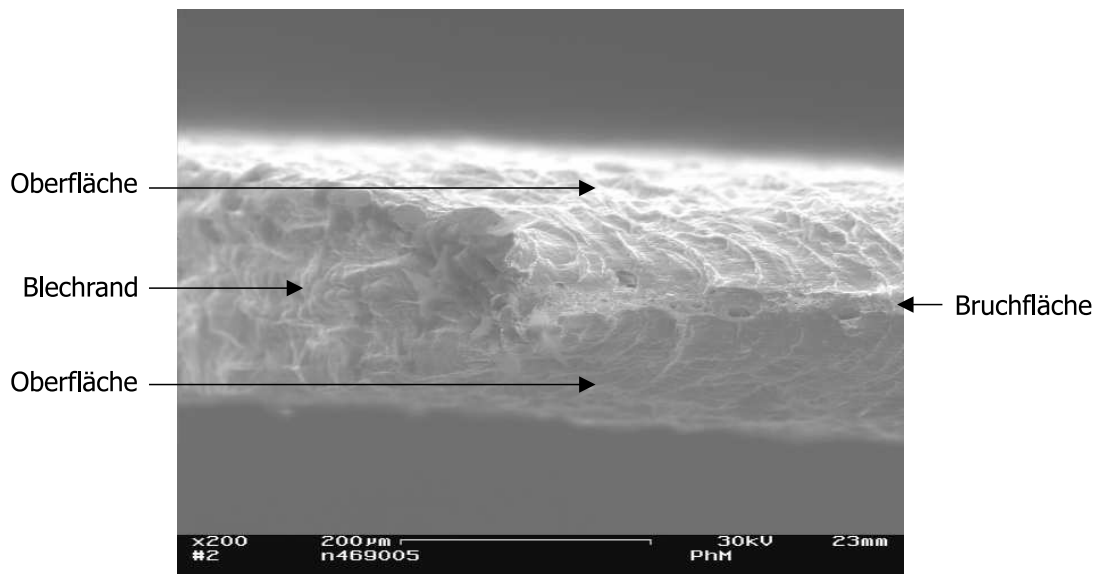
Aufsicht (entlang der Zugrichtung) auf die Bruchfläche des dünnen Randes der keilförmig geschliffenen Zugprobe des Blechs 3.
